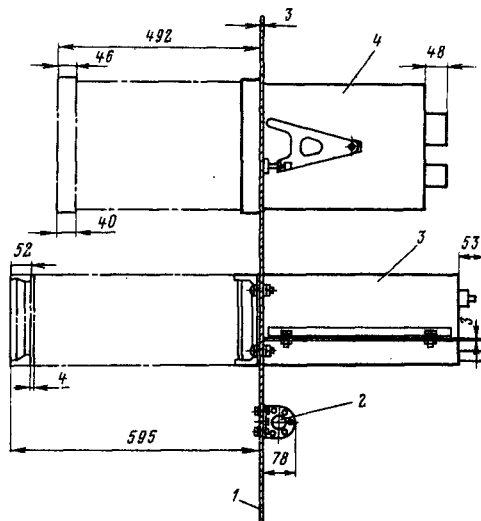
Установочный чертеж комплекта газоанализатора ГИАМ-5:
